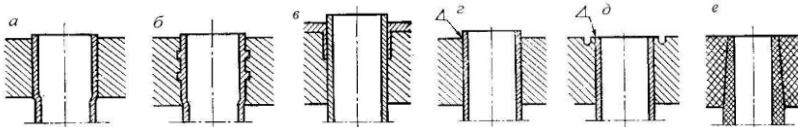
Способы крепления труб в трубной решетке. *а, б* – развальцовка, *в* – пайка, *г, д* – сварка, *е* – склейка.
